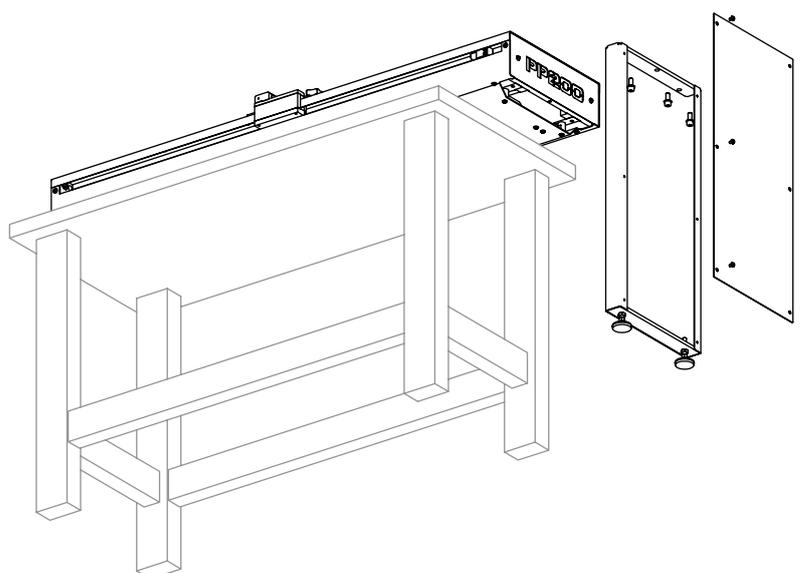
Montaje del Pie de la Estructura al Cuerpo principal
